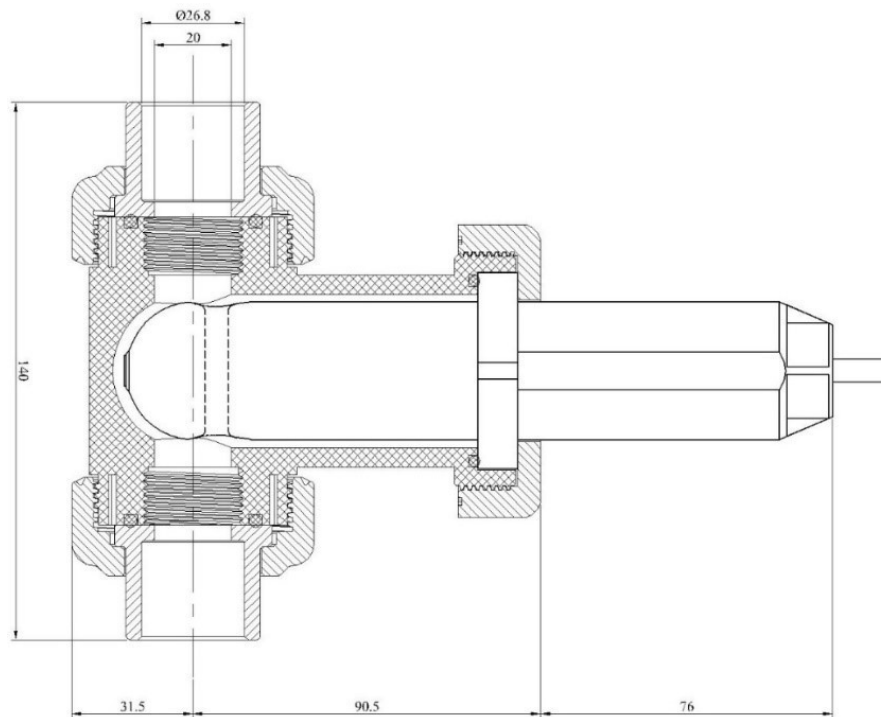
Dimensiones del sensor HM-500/510/520 y del conjunto en T ST-001 (mm)
